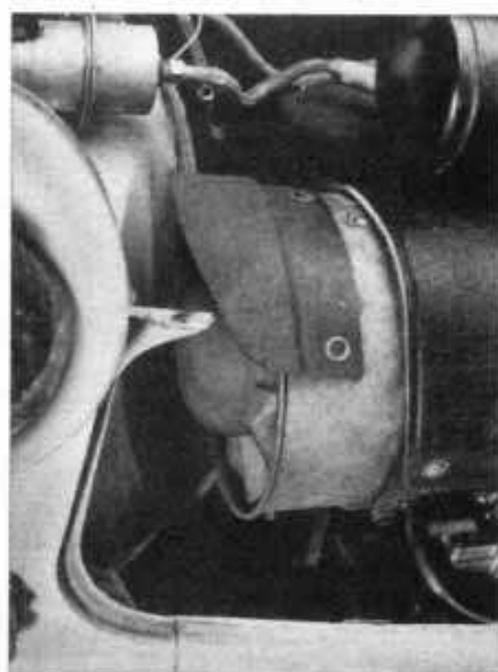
Kühllüfter des Trabantmotors, der nicht mehr mit Spannbänd, sondern mit einer Verschraubung befestigt wird
